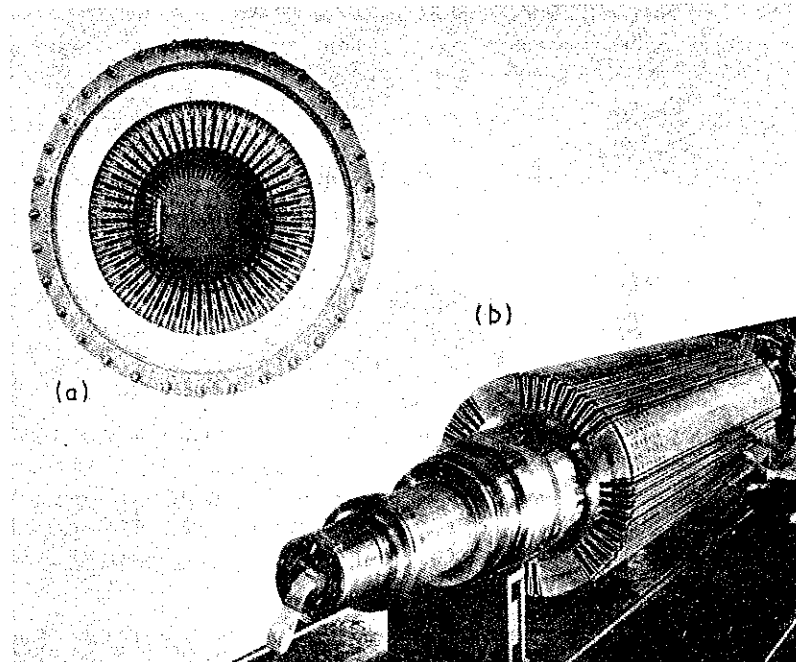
(a) Núcleo del estator para un generador de turbina de c-a. (b) Rotor de un generador de turbina de cuatro polos. (Cortesía de Allis-Chalmers Manufacturing Company.)
